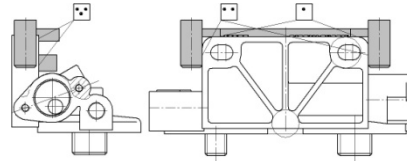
Схема базирования детали «Корпус ФТ 040.1117 110»
